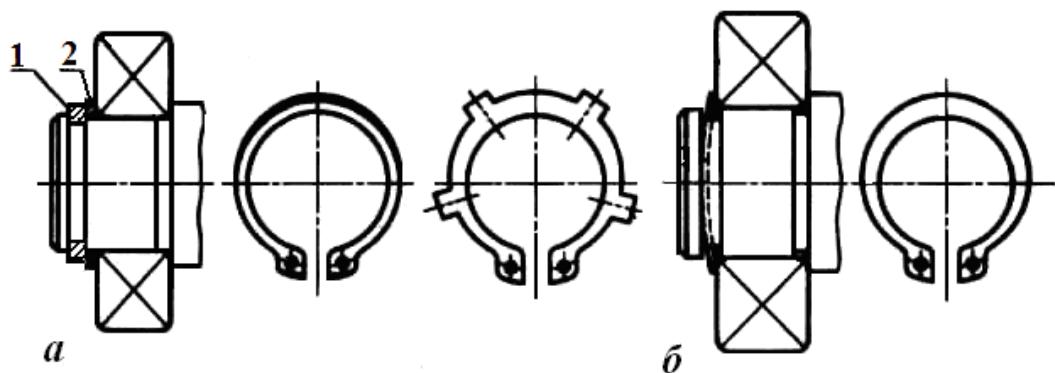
Способы крепления подшипников на валу: а - плоскими кольцами и б -изогнутыми кольцами
